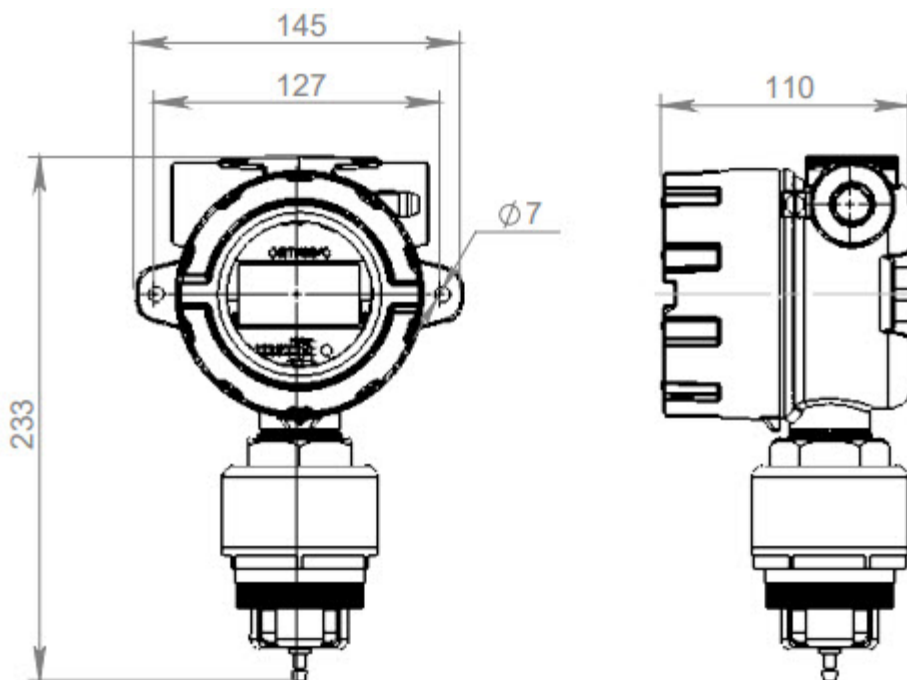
Габаритный чертёж изделия с 3-я вводными отверстиями
